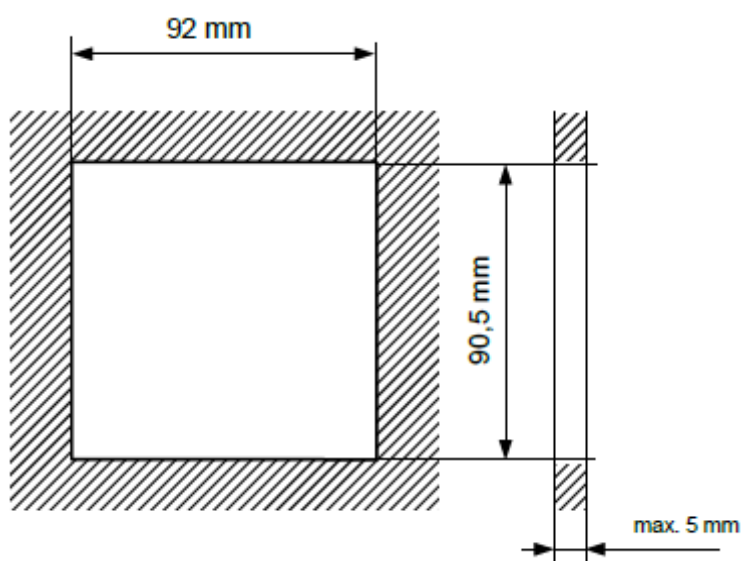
Dimensiones permisibles del orificio de montaje
